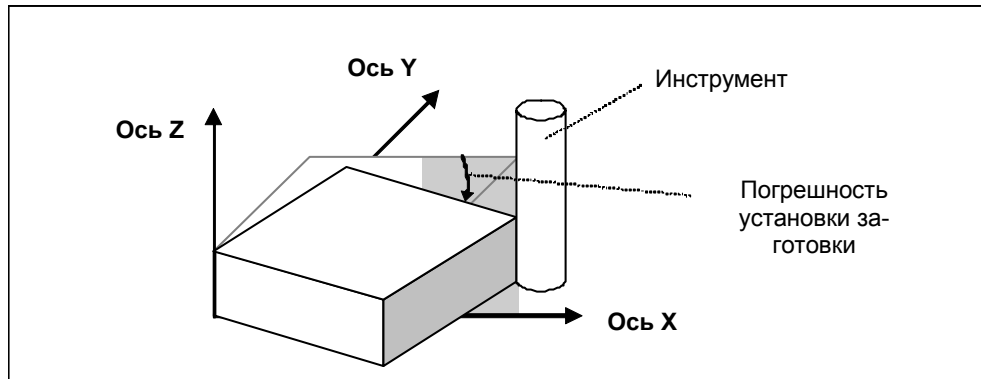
(р) Коррекция на режущий инструмент, когда имеется только погрешность установки заготовки относительно оси Z (если RCM=0)
